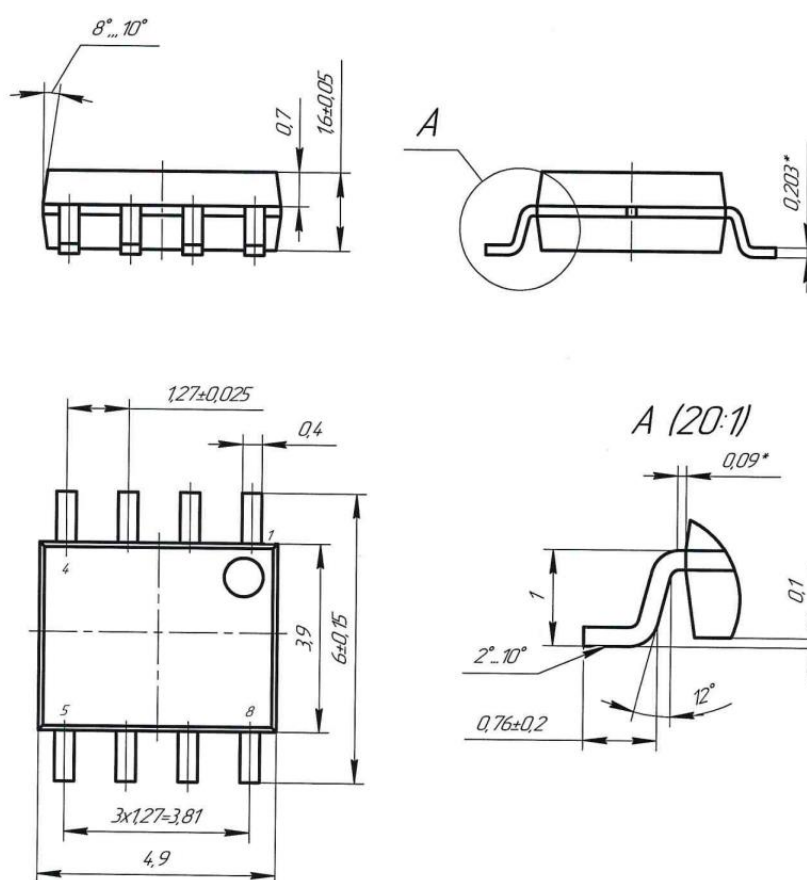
Габаритный чертеж корпуса 4303.8-DH3 К (размеры в мм)
